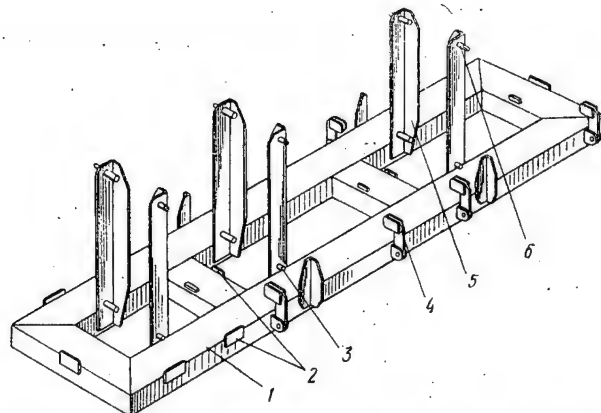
Приспособление для сварки фланцев блока.
